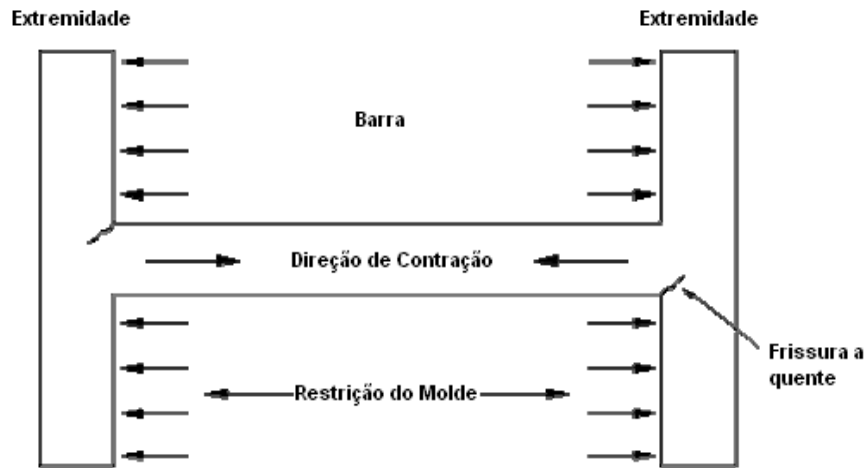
Surgimento de fissuras a quente na fundição de uma barra metálica.
